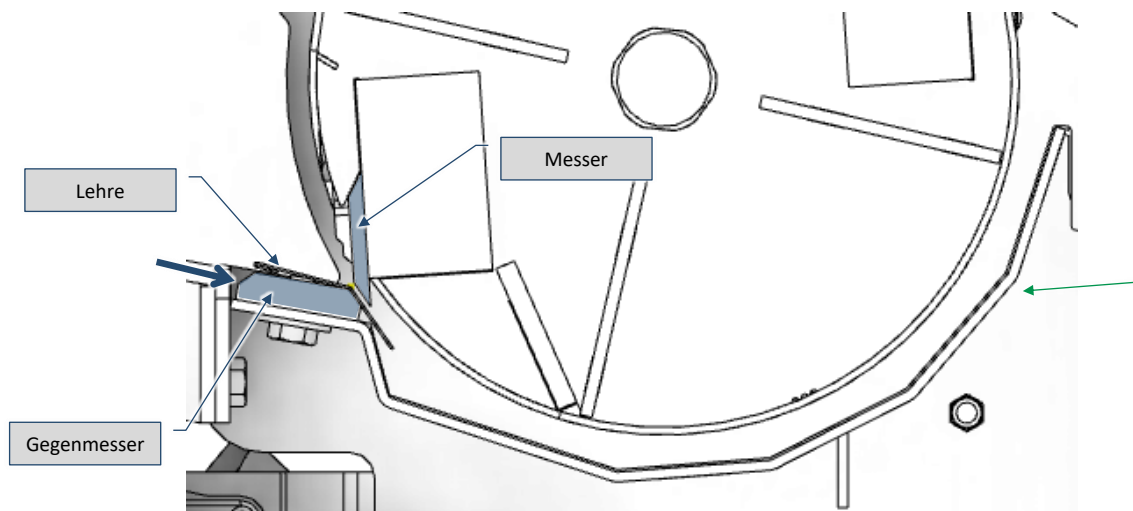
Einstellung des Gegenmessers (Schnittansicht)
